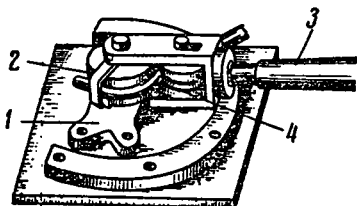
Ручное приспособление для гибки труб с двумя роликами для обкатки
